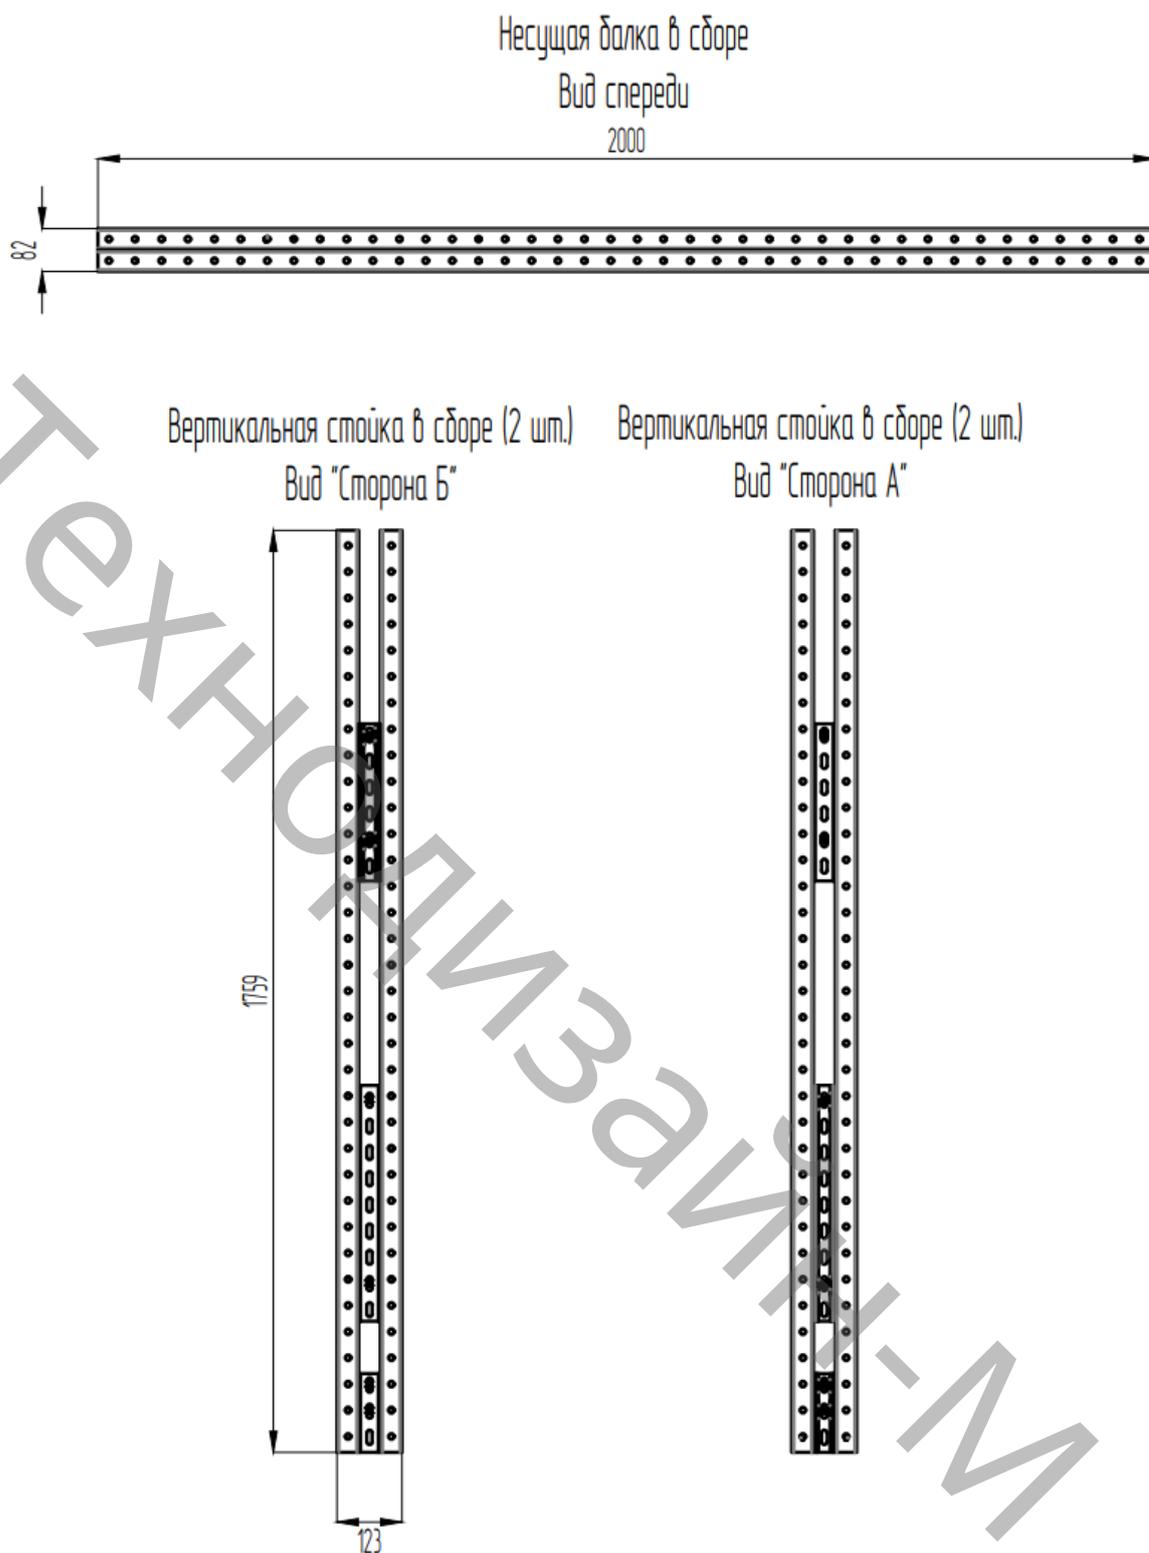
Общий вид несущей балки с сборе и вертикальной стойки в сборе.
